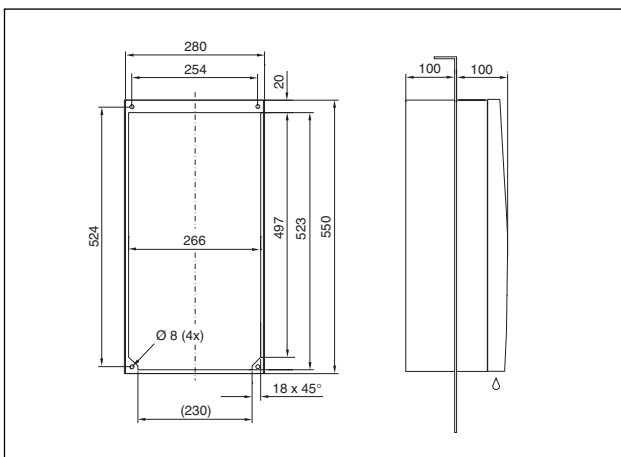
SK 3303.xxx, SK 3361.xxx Delinbyggnad
